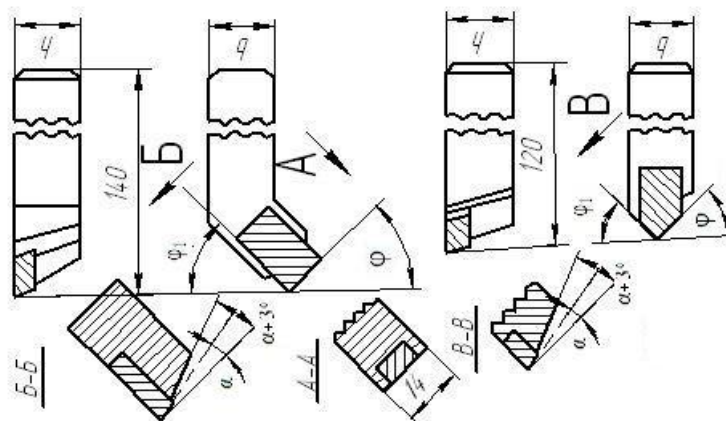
Різець оздоблений керамічною пластиною
